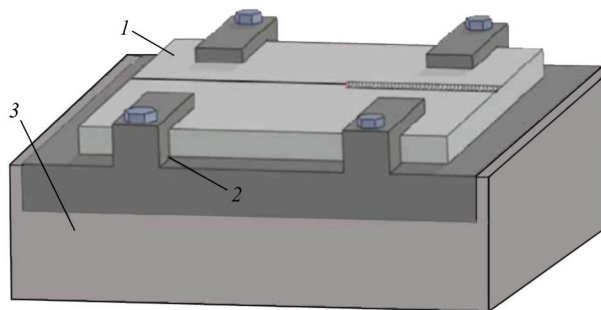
Конструктивна схема пристрою для попереднього підігріву зразків: 1 — зразок для зварювання; 2 — притискні кронштейни; 3 — піч із нагрівальною спіраллю
